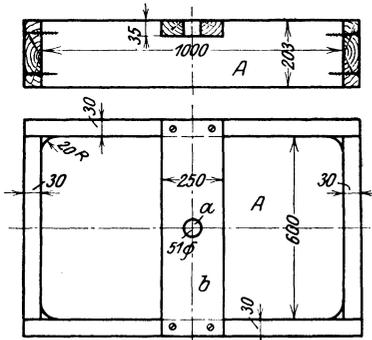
Rechteckiger Kasten zu Fig. 122.
